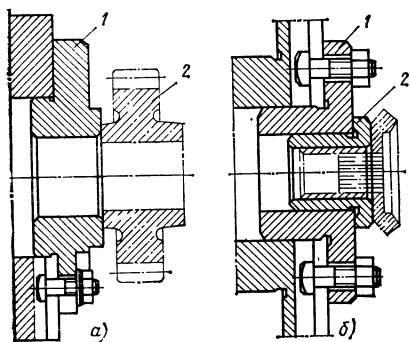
Приспособления для протягивания отверстий в деталях с обработанным торцом
